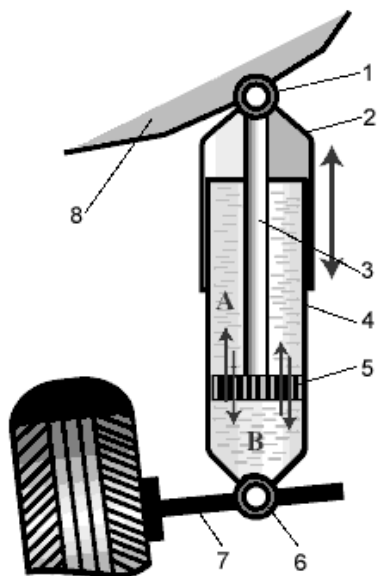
Схема амортизатора 1 - верхняя проушина; 2 - защитный кожух; 3 - шток; 4 - цилиндр; 5 - поршень с клапанами сжатия и «отбоя»; 6 - нижняя проушина; 7 - ось колеса; 8 - кузов автомобиля
